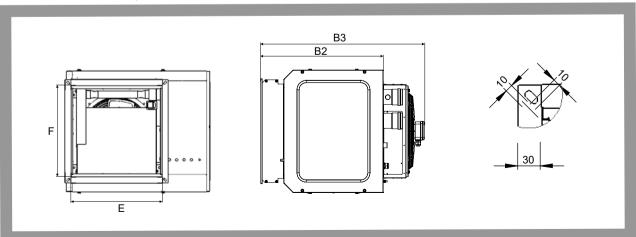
Размеры воздухонагревателя MONZUN, с фланцем
